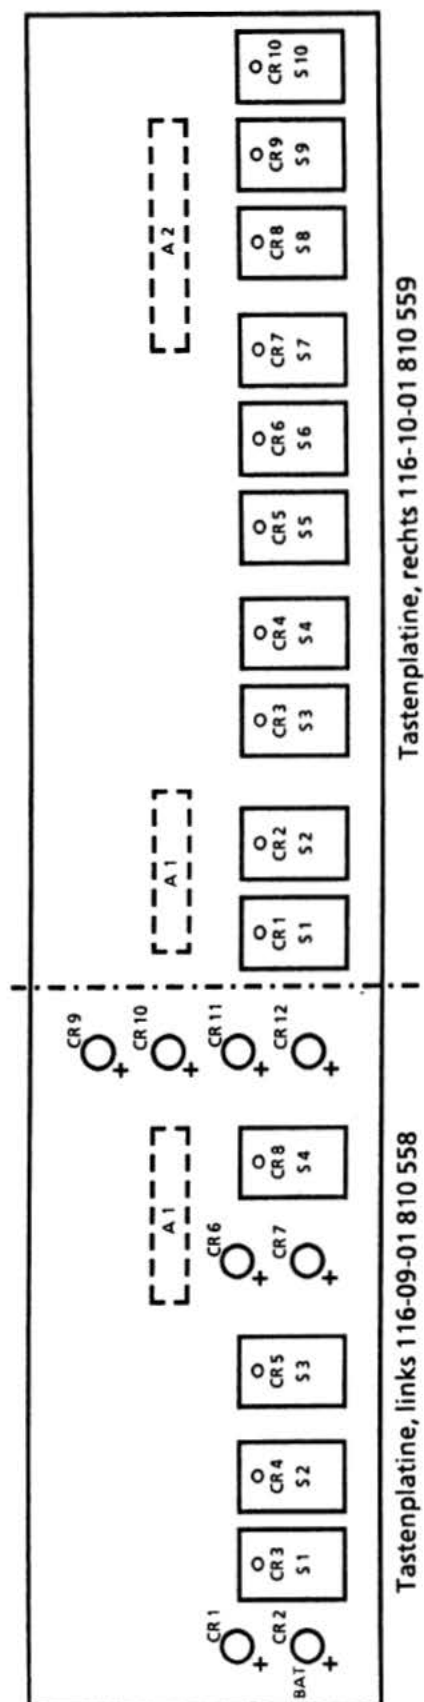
Tastenplatine, Bauteil-Lageplan
